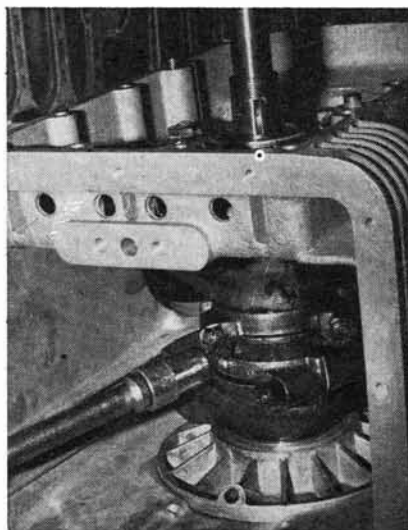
Serrage des écrous de bielles (Photo RMT)
